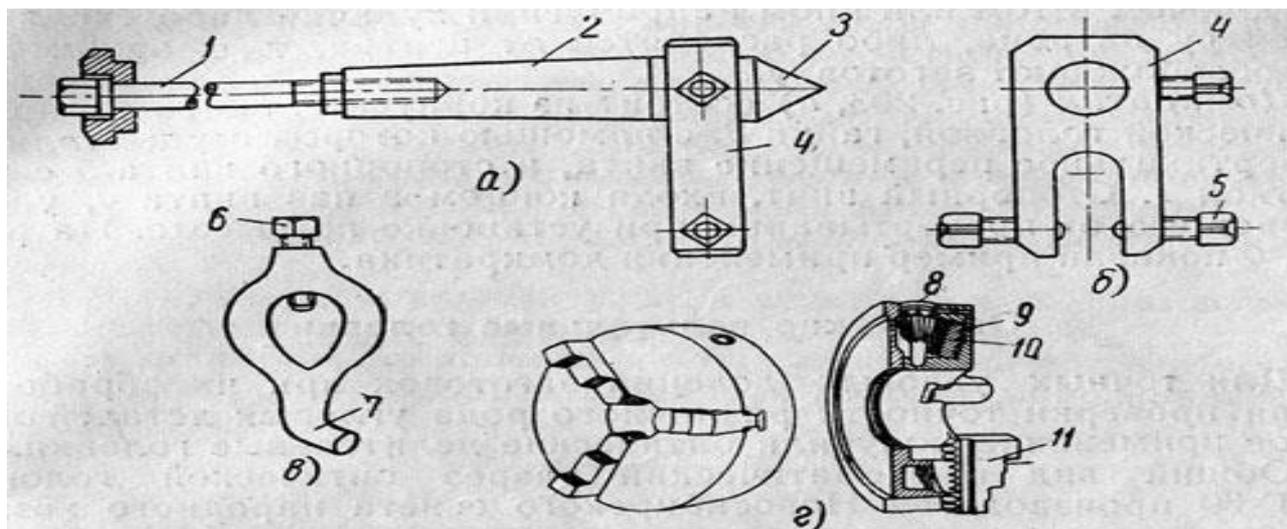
Приспособления для закрепления заготовок в делительной головке
